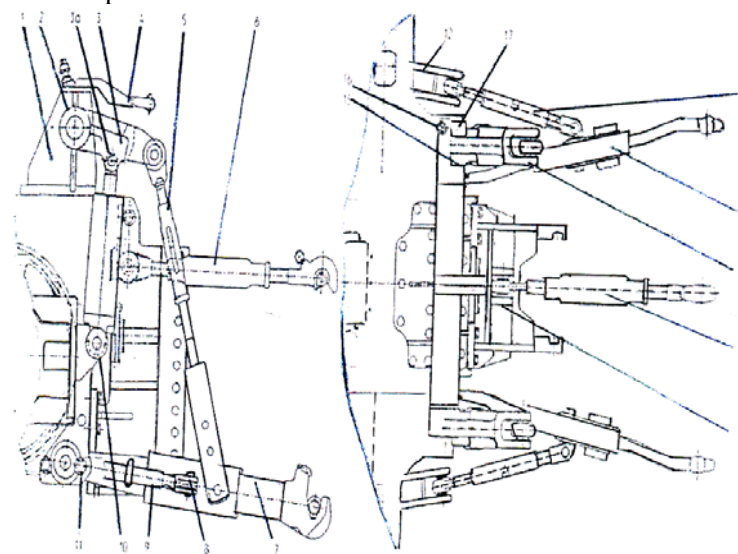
а – Заднее навесное устройство трактора «Беларус 2522»: 1 – кронштейн поворотного вала; 2 – поворотный вал; 3 – наружные рычаги (левый и правый); 3а – пальцы штоков гидроцилиндров; 4 – гидроцилиндры; 5 – раскосы; 6 – верхняя тяга; 7 – нижние тяги; 8 – проушины; 9 – стяжки; 10 – пальцы; 11 – гидроцилиндры и кронштейны нижних тяг; 12 – кронштейны стяжек; 13 – пальцы (силовые датчики); 14 – кронштейн крепления верхней тяги; 15 – кронштейн датчика позиционного; 16 – датчик позиционный
